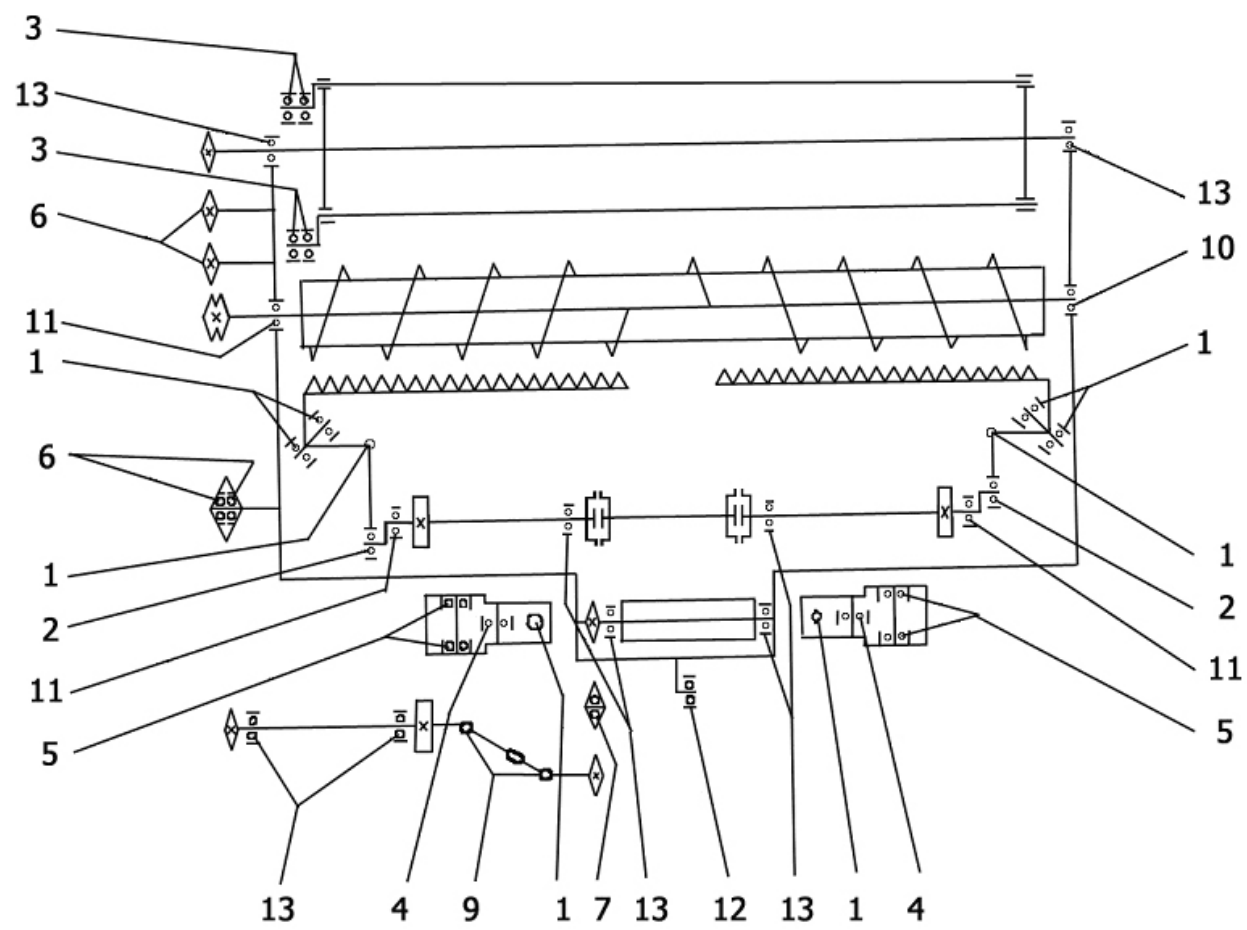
Схема расположения подшипников жатки травяной РСМ-100.70 к комбайну «Дон-680».
